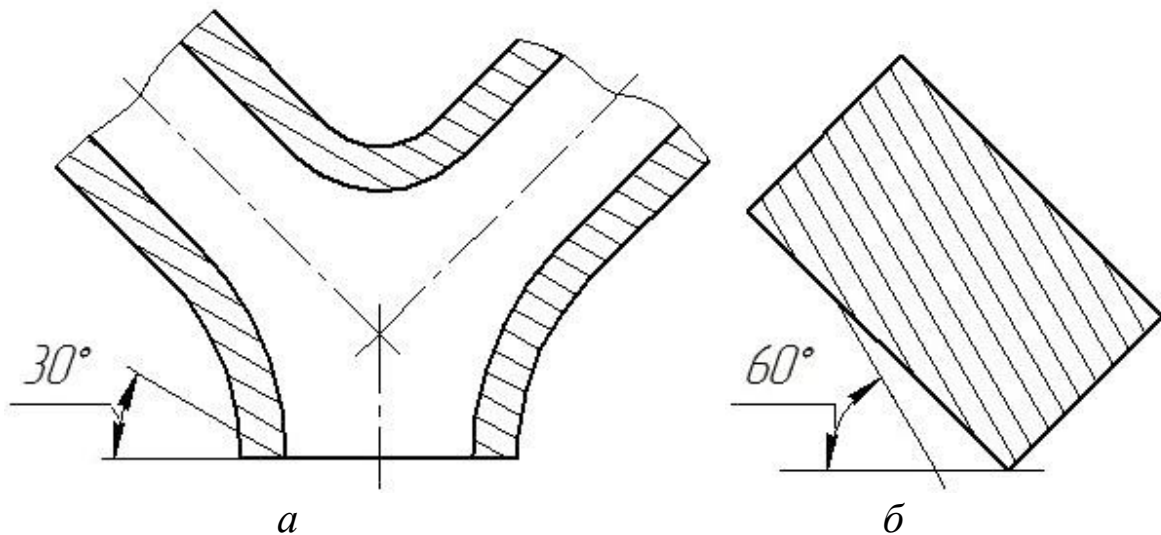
Нанесение штриховки под углами 30° и 60°
